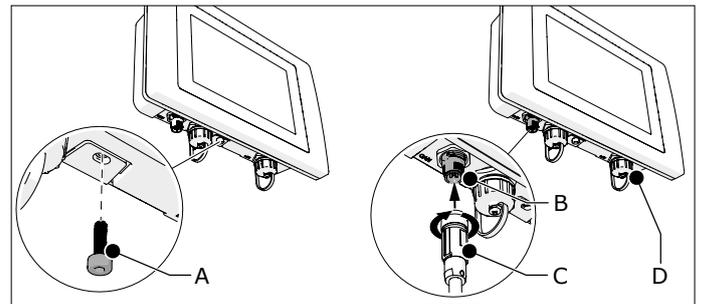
Sicherungsschraube und HMI-Kabel
